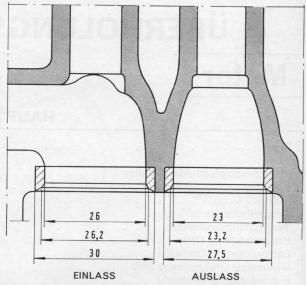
Durchmesser der Ein-und Auslassventile im Zylinderkopf.
